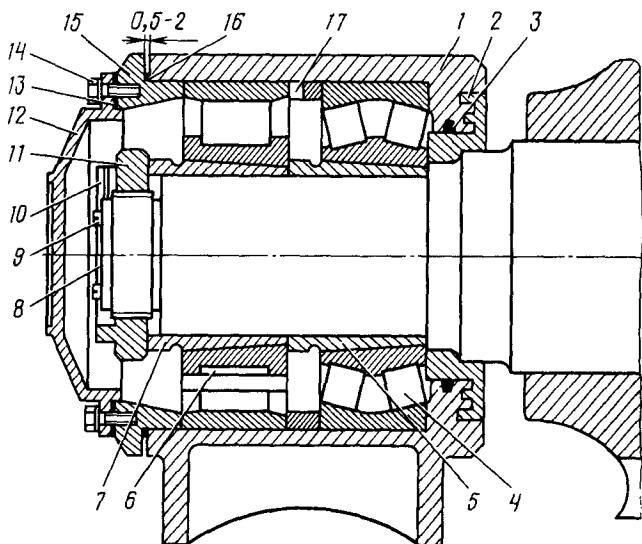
Букса со сферическим и цилиндрическим подшипниками на втулочной посадке:
